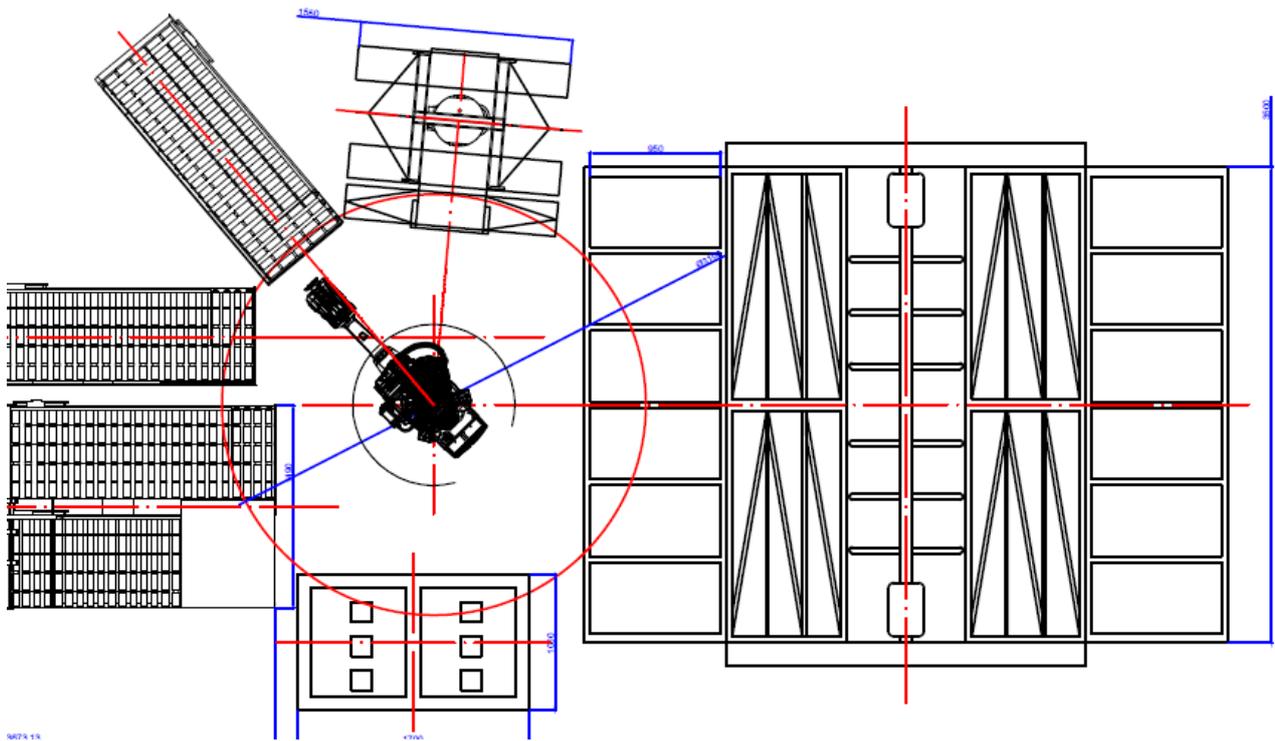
Planimetria proposta C.2: un solo robot al centro con trasferimento della zona di assemblaggio e del magazzino verticale
